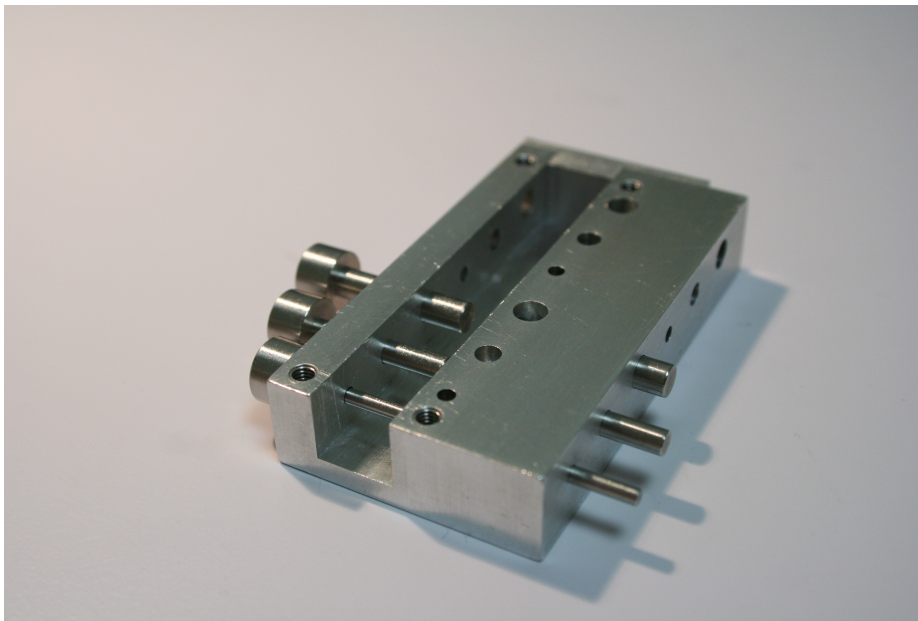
Photo du moule permettant de fabriquer des fantômes à inclusion.
